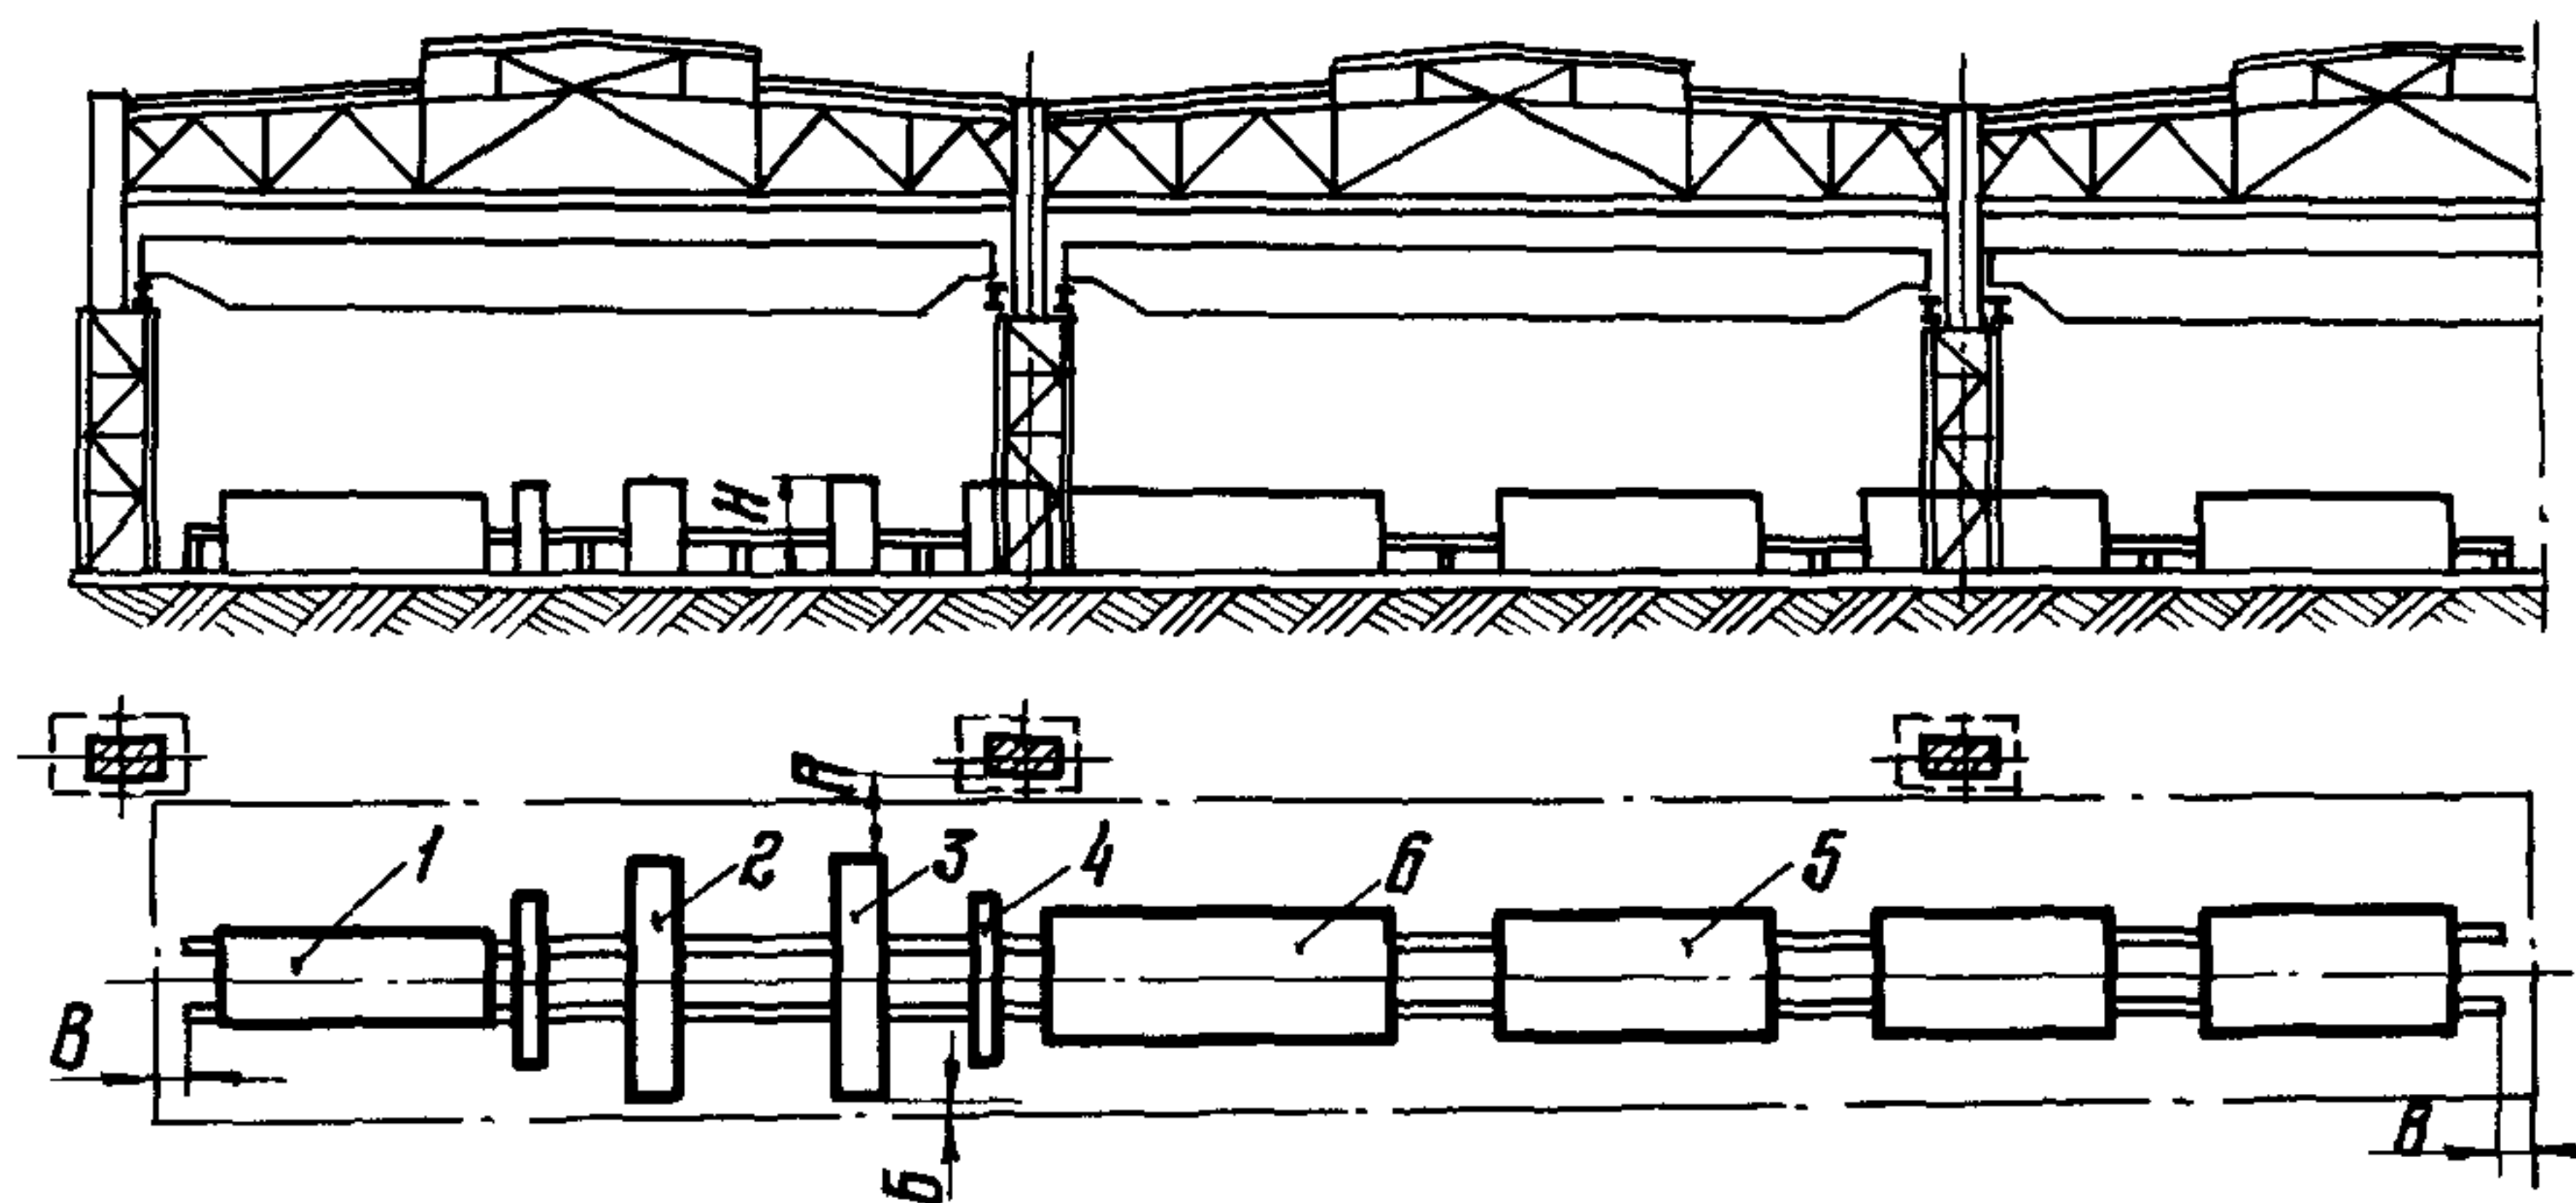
Размещение поточной линии для сборки и сварки подкрановых балок:
